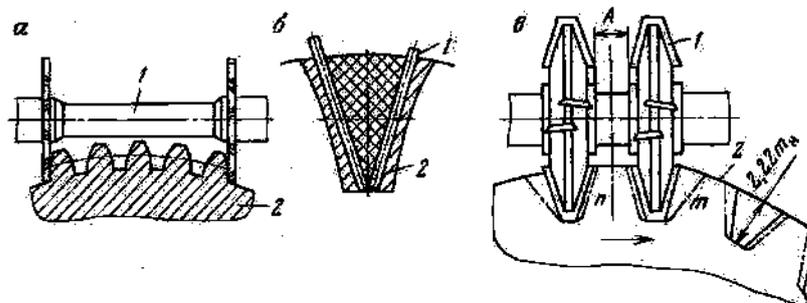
Схемы прорезания двумя трехсторонними дисковыми фрезами (1) зубьев заготовок зубчатых колес (2):
